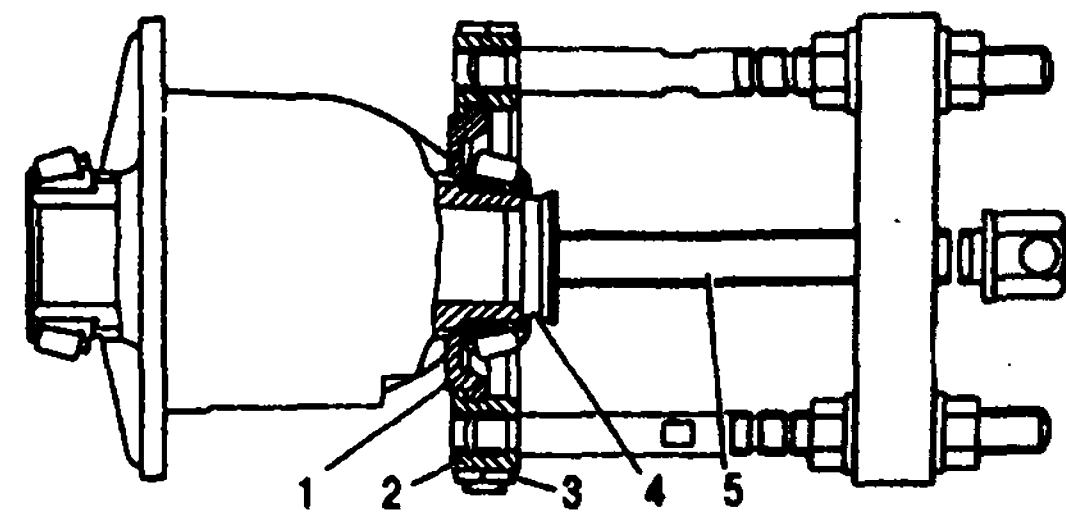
Снятие внутреннего кольца подшипника дифференциала: 1 - вкладыш; 2 - опора; 3 - гайка; 4 - подпятник; 5 - винт
